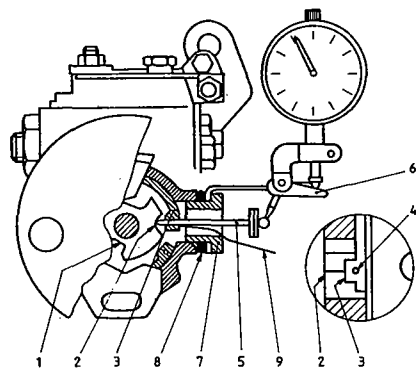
Montaje del comparador con una herramienta de soporte especial a través del orificio de inspección.
